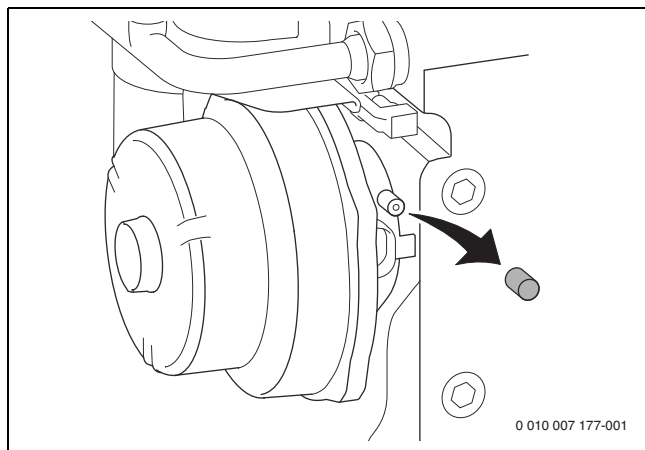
Tubulure de mesure sur le dispositif de mélange
